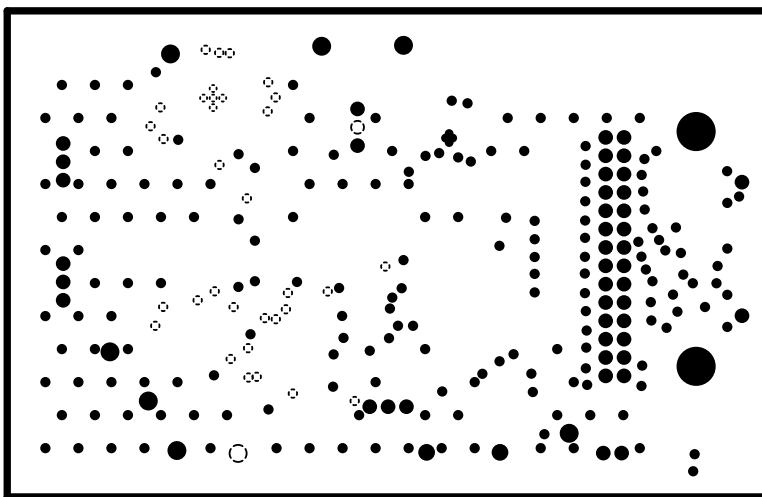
ADS1282EVM 的 PCB 布局 (内部 AVSS 平面)
